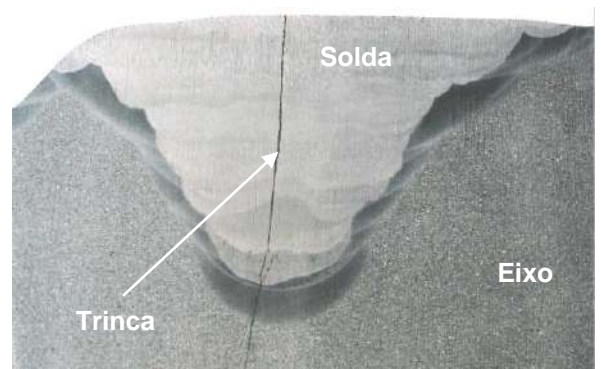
Corte transversal de eixo recuperado por soldagem deficiente, com trinca iniciada na solda e, em outra posição, fratura iniciada na ZTA.
